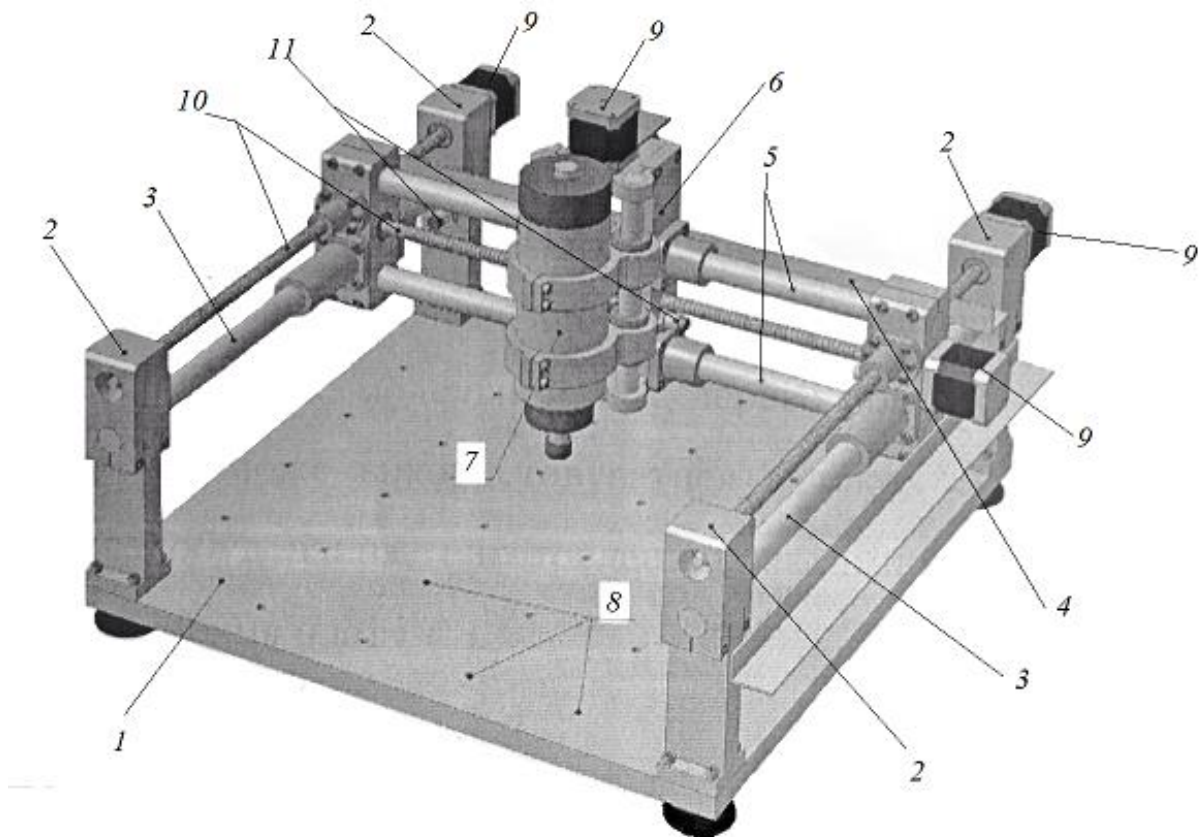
Малогабаритний настільний фрезерний верстат портального компонування «CNC 500»
